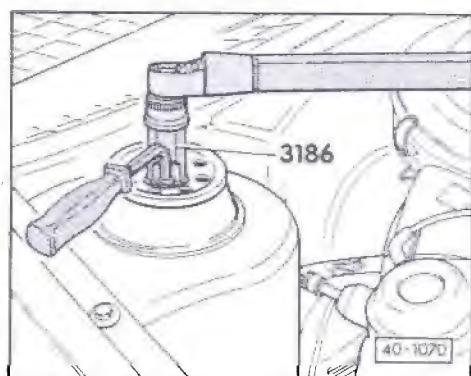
Jambe de force : vissage et dévissage sur carrosserie
